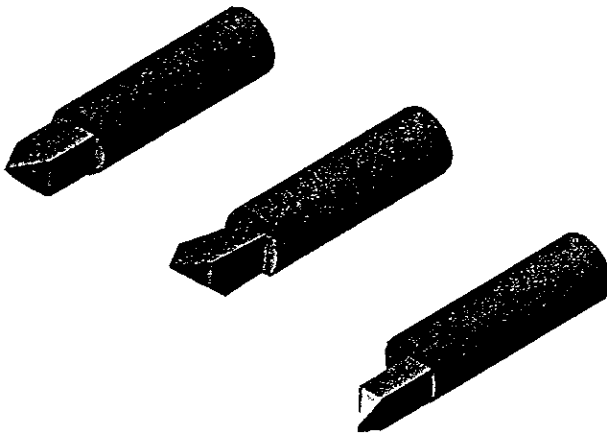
Herramientas utilizadas en el centro de maquinado.
